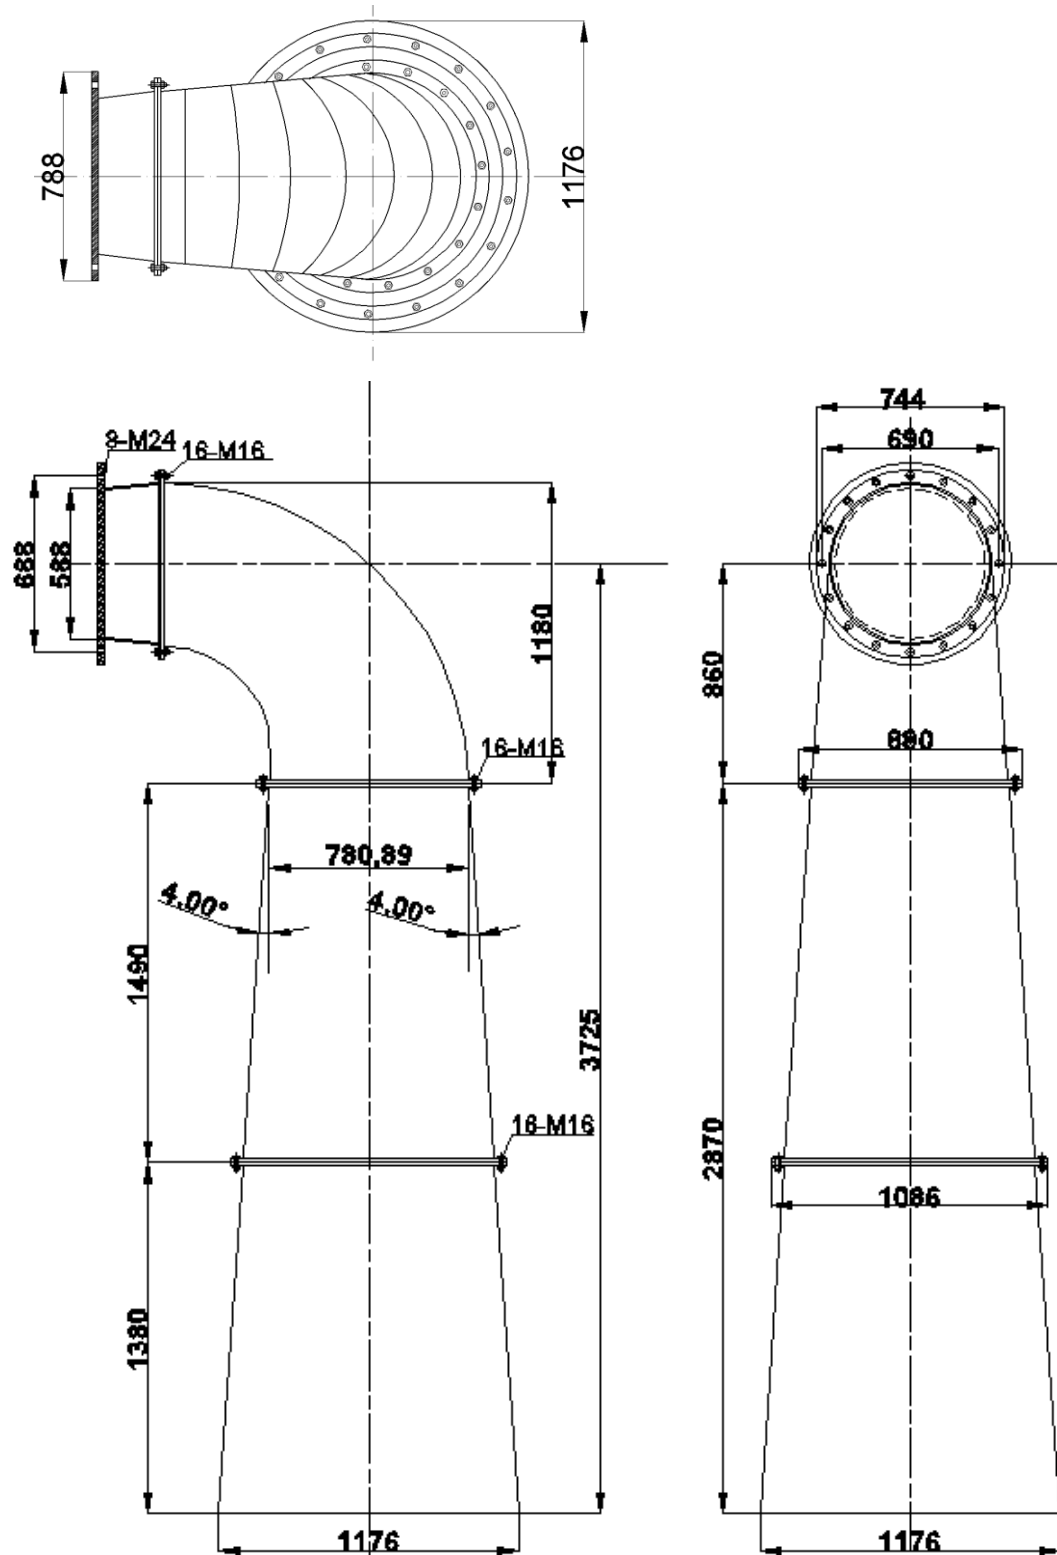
Layout Dimensi Utama *Draft Tube* Turbin Francis poros horisontal
